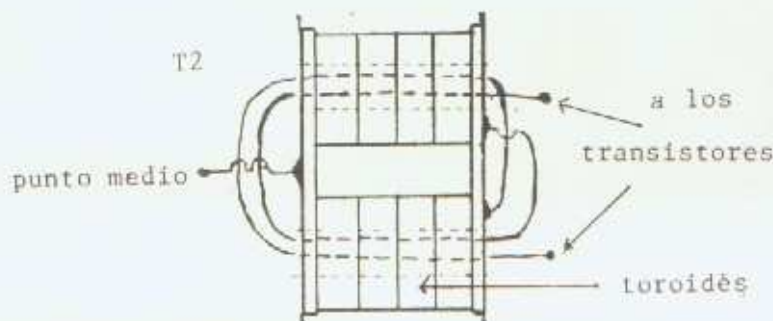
Detalle constructivo y de conexionado de la derivación central.
